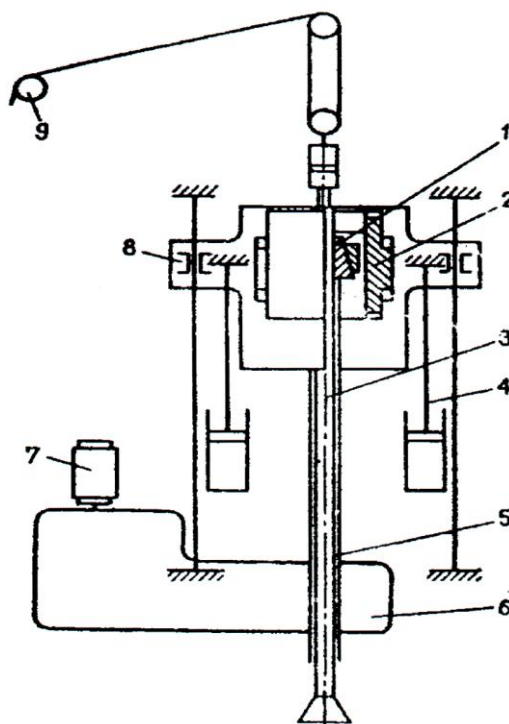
Кинематическая схема вращательно-подающего механизма станка 2СБШ-200Н: 1 – зажимные кулачки; 2 – зажимной патрон; 3 – штанга, 4 – шток гидроцилиндра подачи; 5 – пустотелый шпиндель гидropатрона; 6 - вращатель (редуктор); 7 – электродвигатель постоянного тока ДПВ-52; 8 – траверса; 9 – лебедка с трехкратным полиспастом для подъема бурового става
